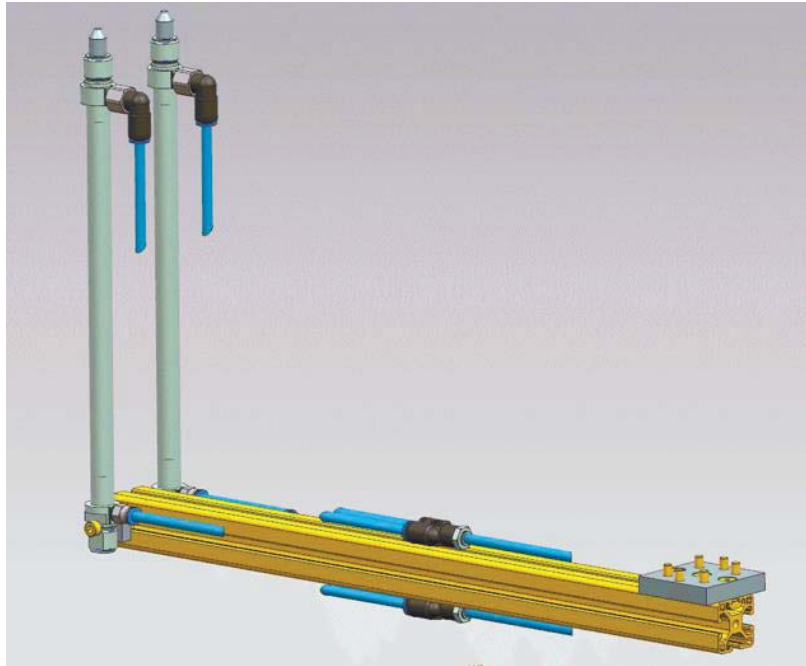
Werkzeug zur Führung beim Fügen der Kolben
